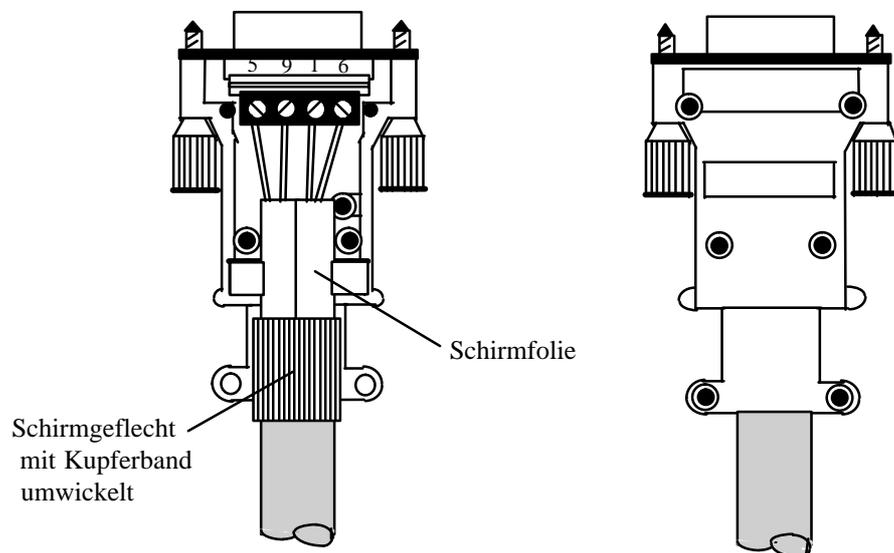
9-poliger Sub D-Stecker mit montierter Standardleitung
